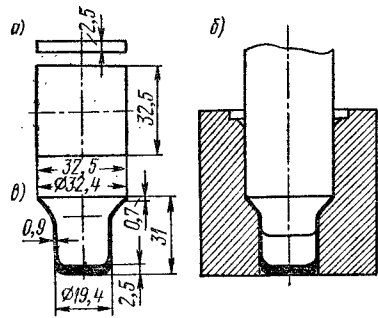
Схема штамповки цилиндрических колпачков из квадратной заготовки: а — заготовка; б — схема штамповки; в — изделие
